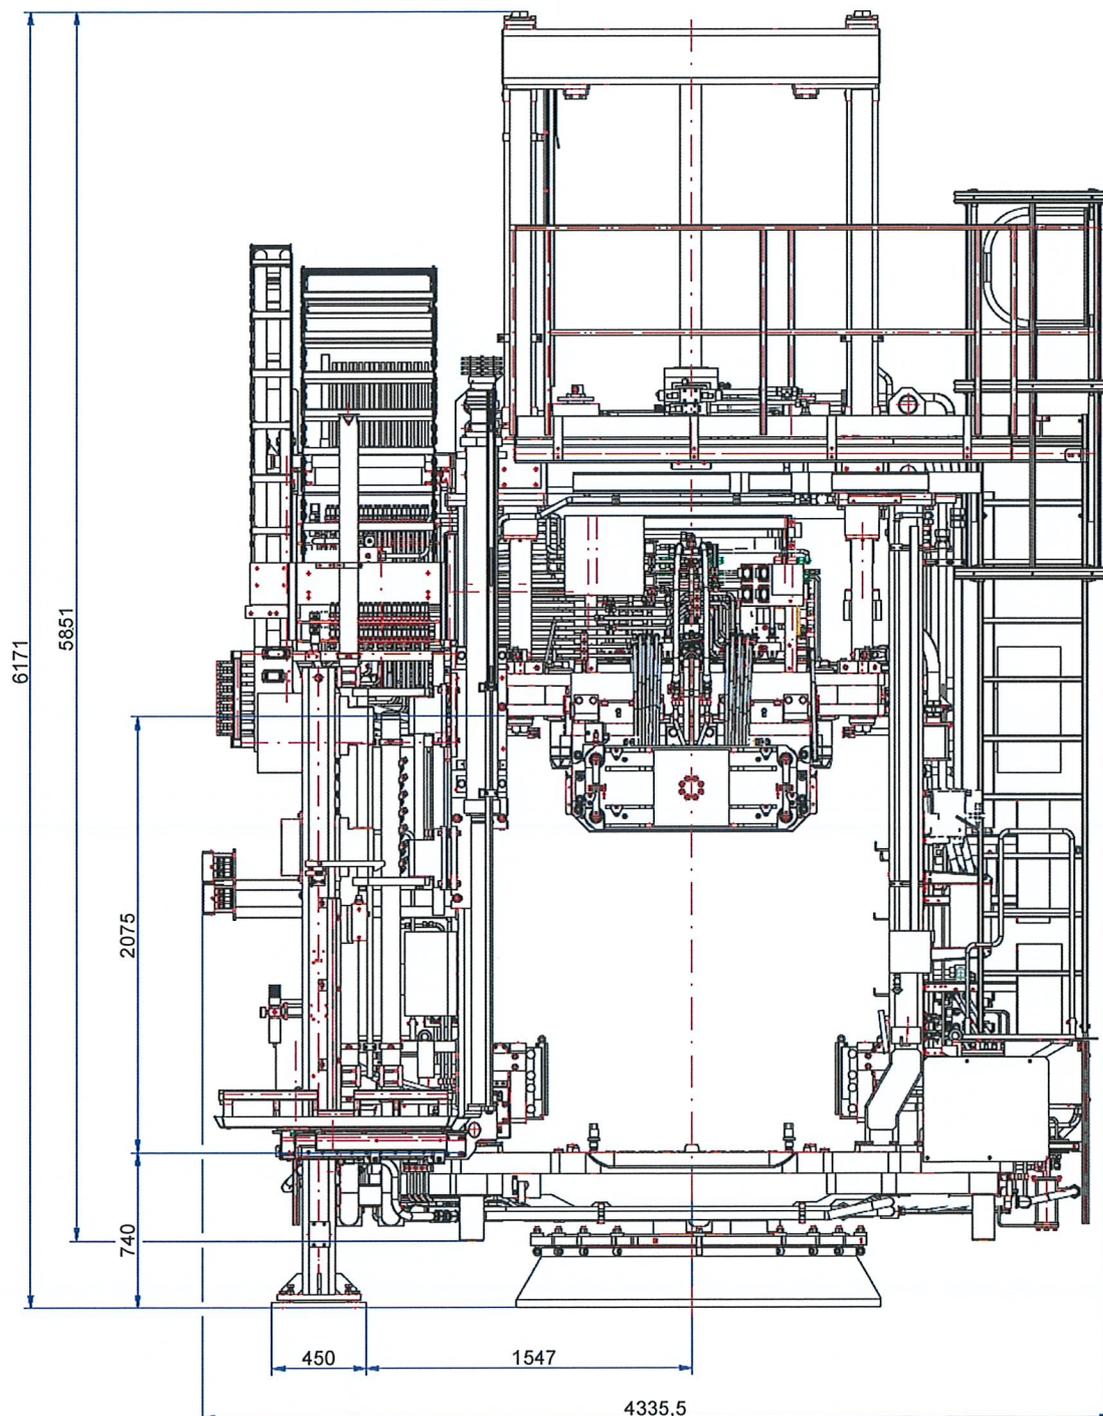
Maschinenlayout mit Gußteilentnahme - Vorderansicht
